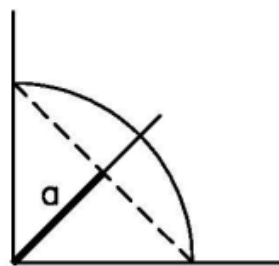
Garganta del cordón de soldadura. Fuente: Catedra de Unión de Materiales por Soldadura.
